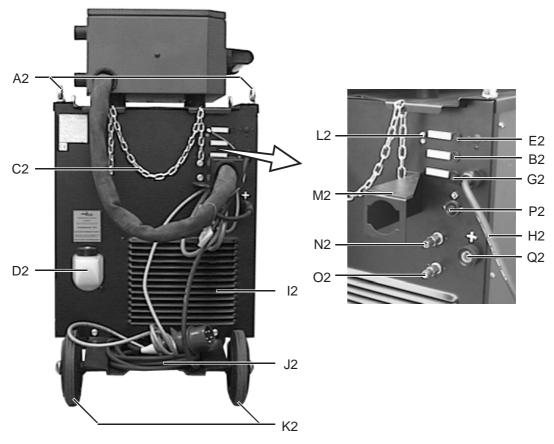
/4; Rückansicht (dekompakte Ausführung)
